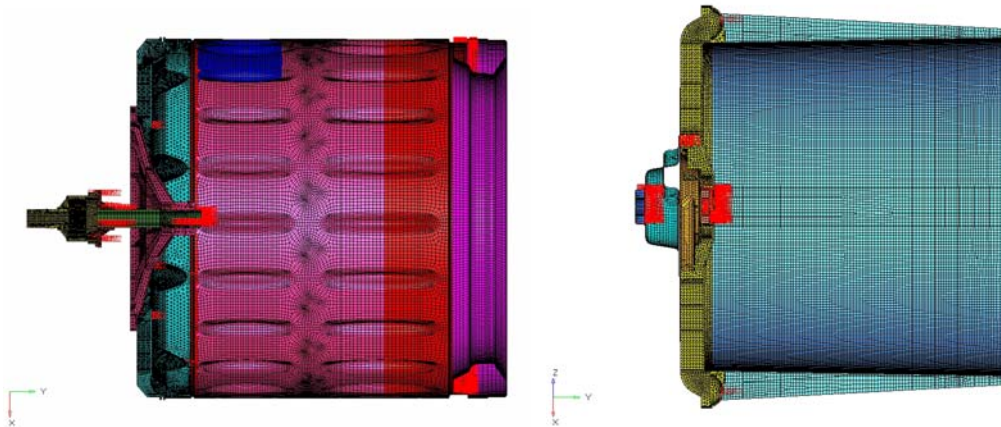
Mallado de rotor (izquierda) y estator (derecha).
